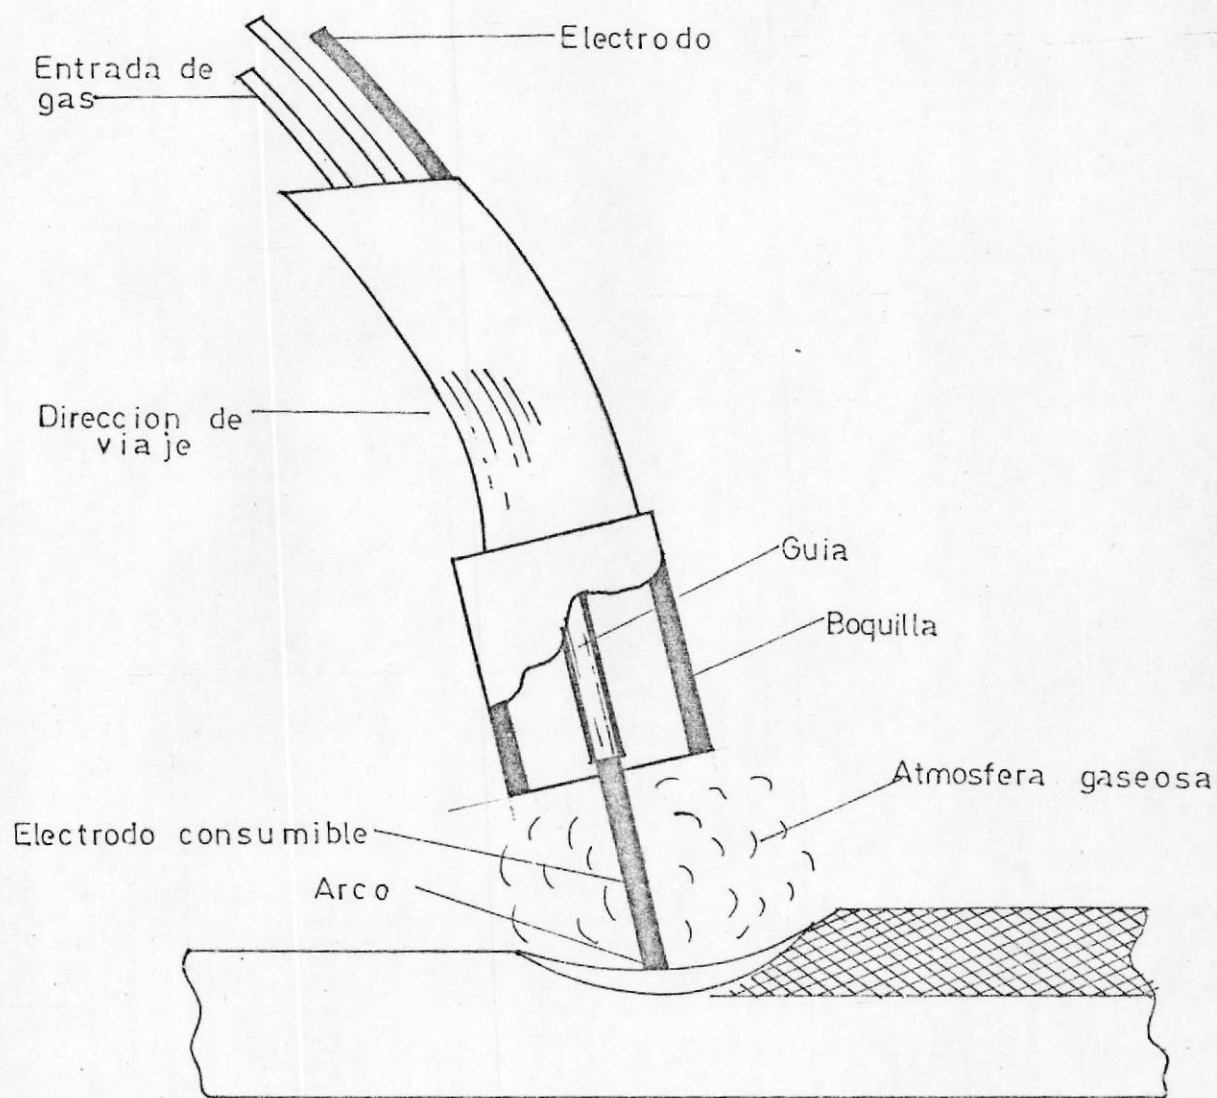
SOLDADURA AL ARCO EN UN PROCESO MIG (6).
